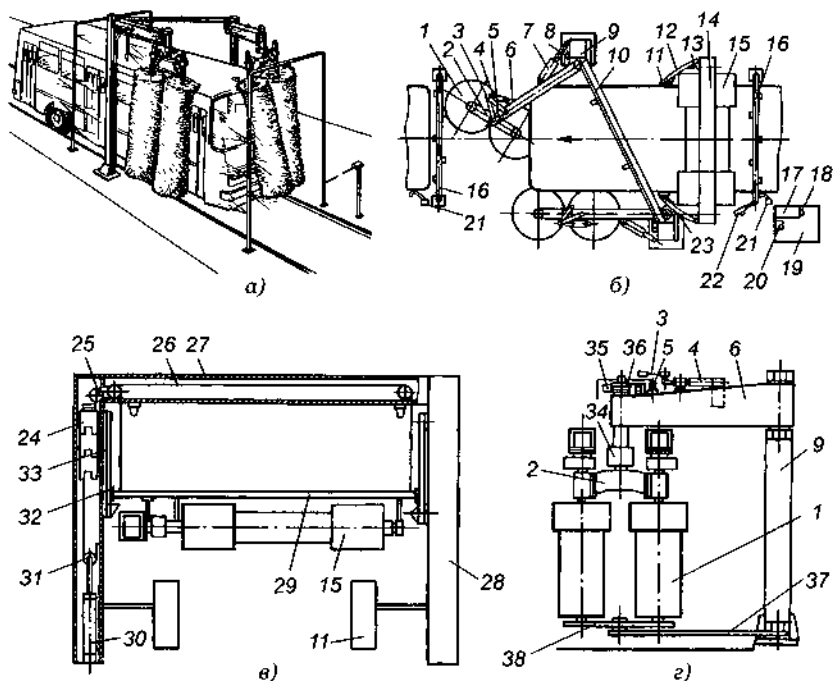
Щеточная установка для мойки автобусов: *а* — общий вид; *б* — вид сверху; *в* — передний блок щеток; *г* — блок вертикальных щеток; 1 — вертикальная щетка; 2 — верхняя траверса; 3 — шарнирный трехзвенник; 4, 30 — пневмоцилиндры; 5 — ограничитель; 6 — верхняя стрела; 7 — пневмоцилиндр управления стрелой; 8 — амортизатор; 9 — колонна; 10, 27 — поперечины; 11 — плоская не вращающаяся щетка; 12 — кронштейн; 13 — пружина; 14 — блок горизонтальной щетки; 15 — горизонтальная щетка; 16 — рамка; 17 — пульт управления; 18 — пневмокран подъема горизонтальной щетки; 19 — кабина оператора; 20 — блок подготовки воздуха; 21 — командоконтроллер; 22 — эжектор; 23, 26 — тросы; 24 — противовес; 25 — система блоков; 28 — стойка; 29 — рамка; 31 — подвижный блок; 32 — ролик; 33 — направляющая рамка; 34 — токоприемник; 35 — пневмокран; 36 — кулачок; 37 — нижняя стрела; 38 — нижняя траверса
